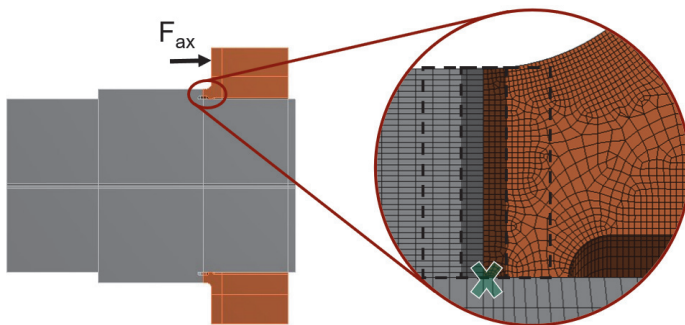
Druckkamm und Ritzelwelle im Schnitt (links) und Kerbengeometrie im Bereich der Schweißnaht (rechts), Kerbe gekennzeichnet
